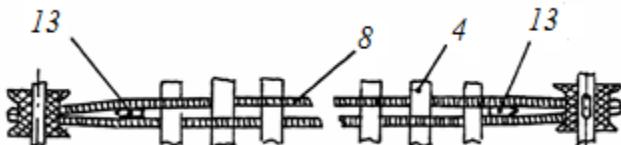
Схема устройства для поворота сортирующих ремней вокруг своей оси (вид сверху)
